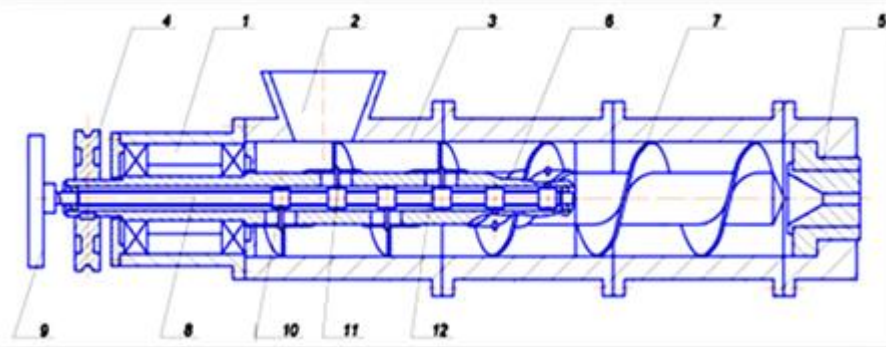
Конструкция одношнекового пресс-экструдера: 1 – подшипниковый узел; 2 – загрузочная воронка; 3 – разъемные корпуса шнековой камеры; 4 – привод; 5 – формующая головка; 6 – шнек; 7 – витки шнека; 8 – резьбовой вал; 9 – приводной механизм; 10 – втулки с установленными пальцами 11; 12 – направляющие
